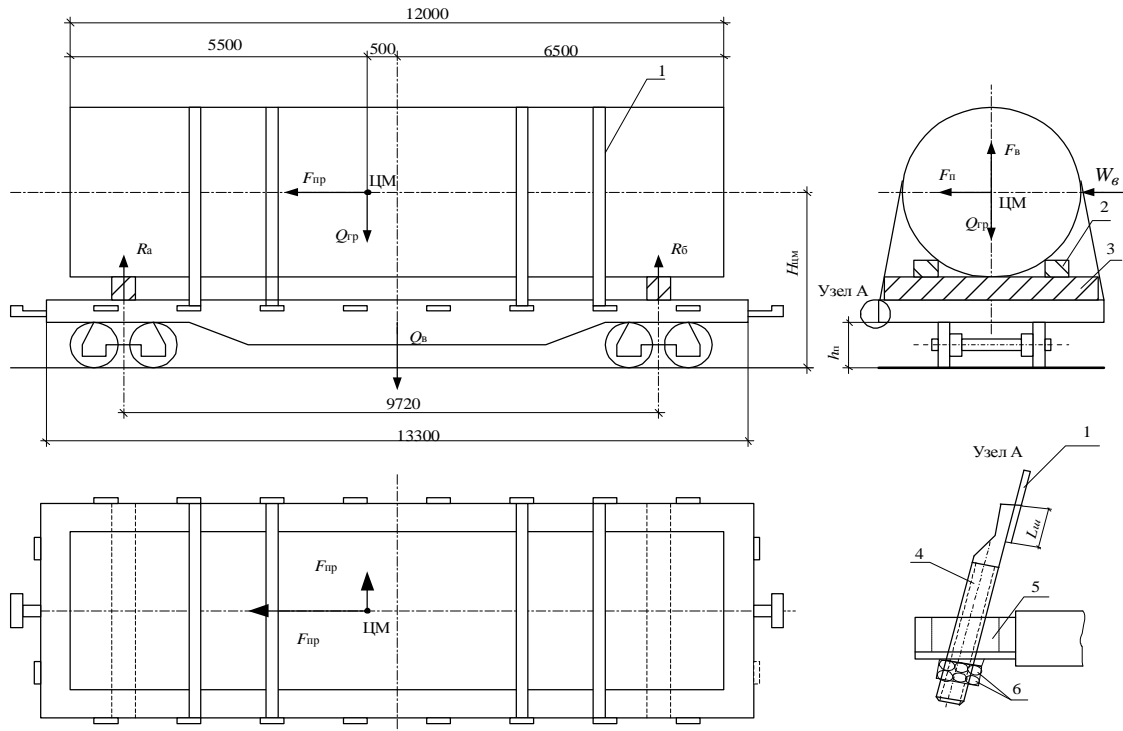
Схема размещения и крепления груза цилиндрической формы:
